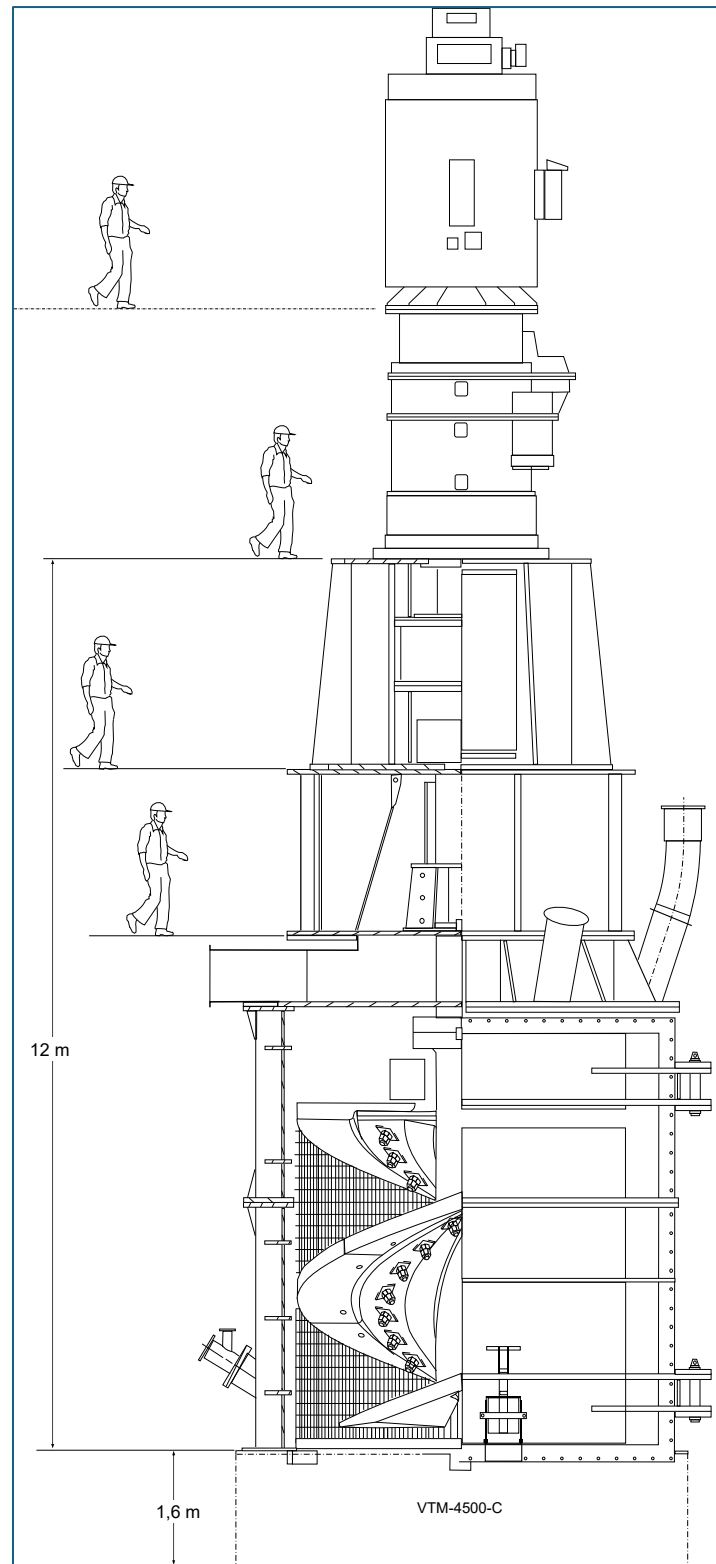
VERTIMILL® Grinding Mill assembly VTM-4500-C
